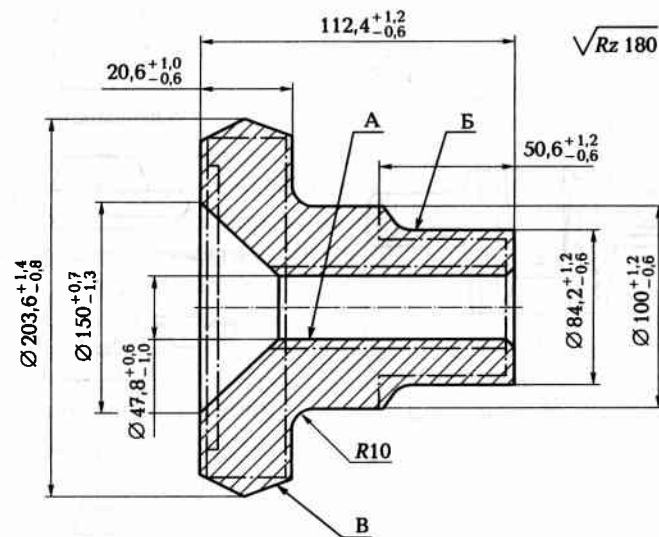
Пример оформления рабочего чертежа штампованной заготовки
